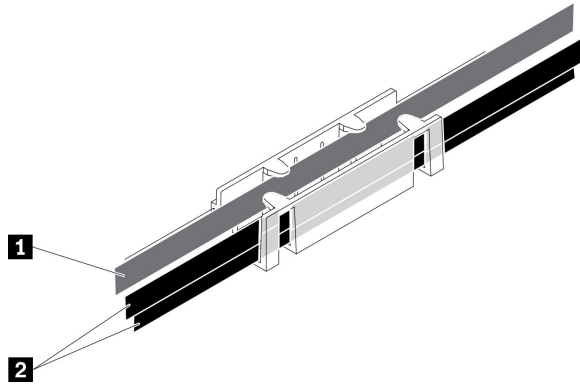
Disposición de los cables del módulo multiconector de NVMe y KVM izquierdo
